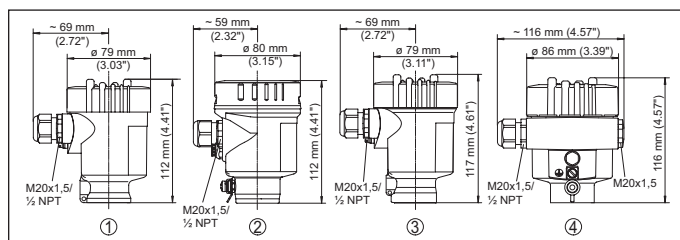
Исполнения корпуса для VEGASWING 61, 63, 66
